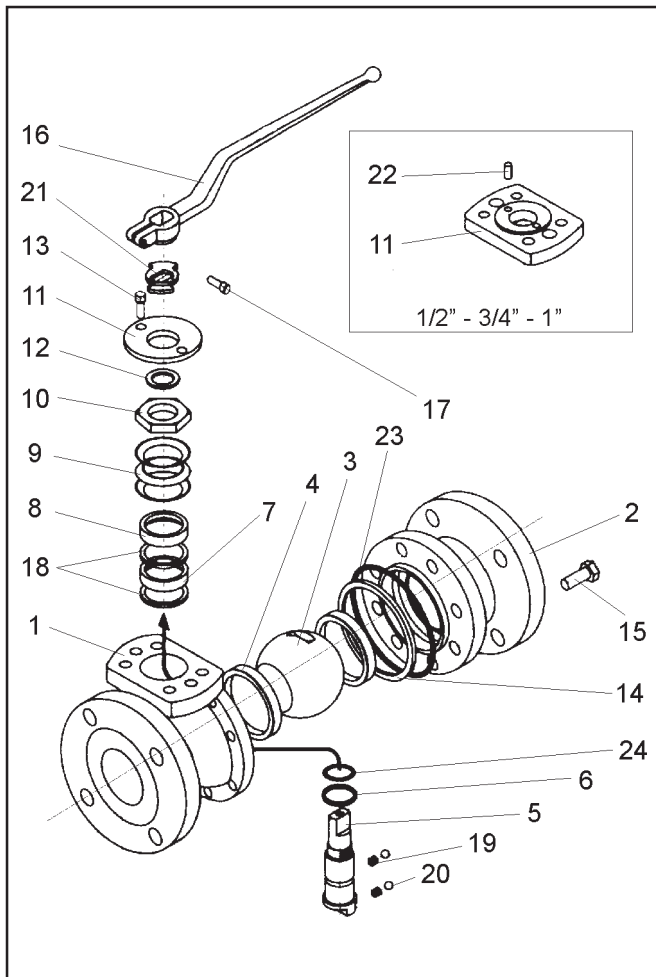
Explosionszeichnung des Kugelhahns BR 76a
